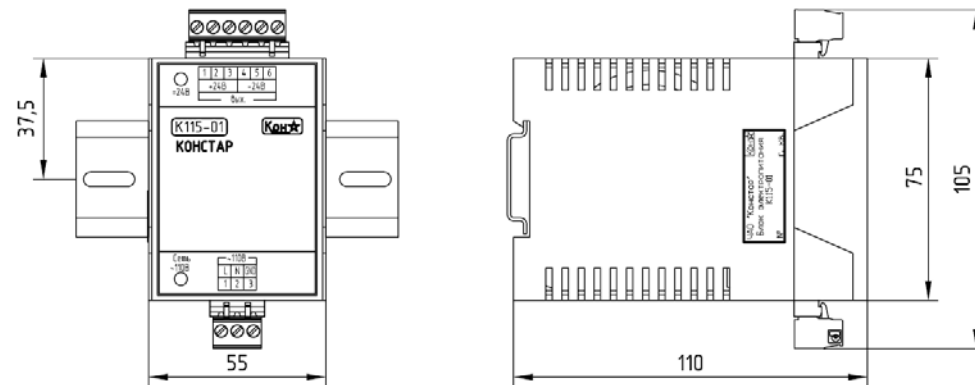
Внешний вид, габаритные и установочные размеры K115-01
